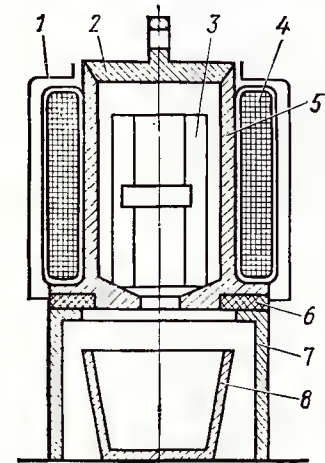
Индукционный нагреватель для выплавки баббита из вкладышей:
